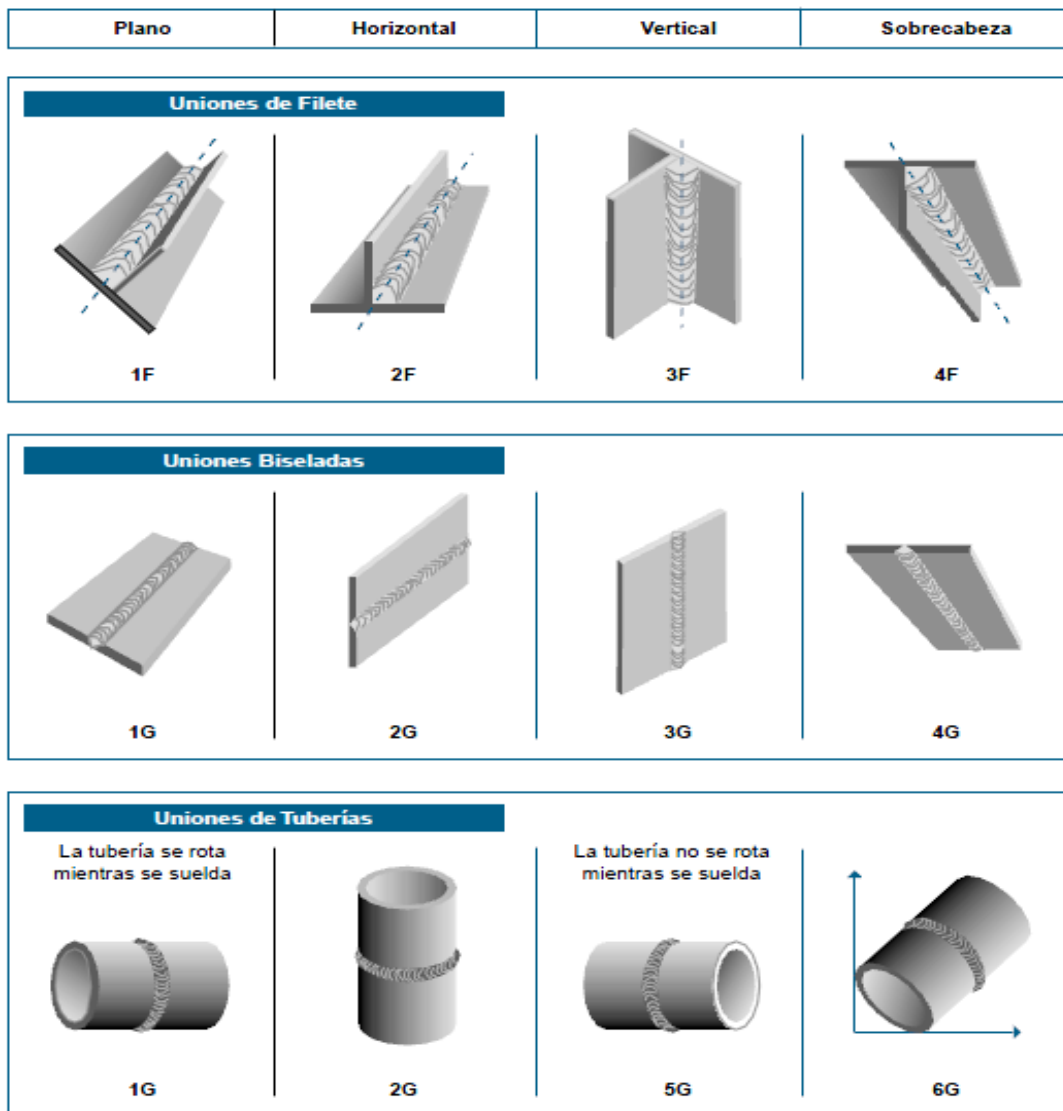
Posiciones de las soldaduras según ANSI/AWS A3.0-8
